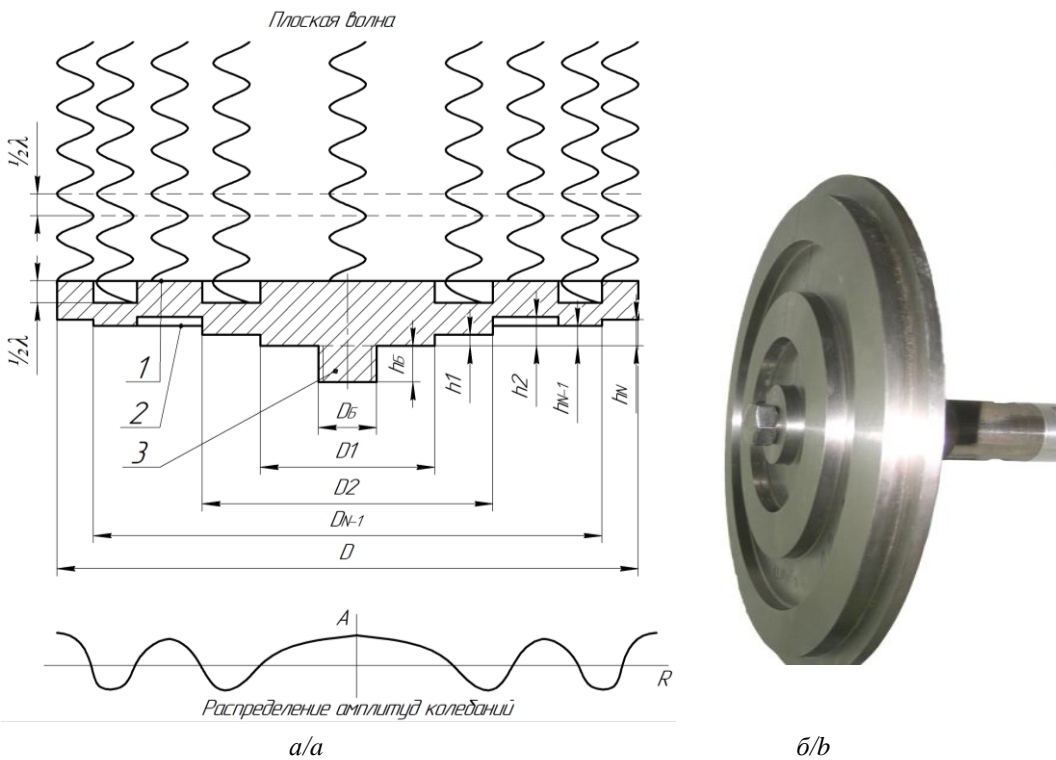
Эскиз (а) и фотография (б) направленного излучателя со ступенчато-переменной поверхностью: 1 – фронтальная сторона; 2 – тыльная сторона; 3 – присоединительный хвостовик
